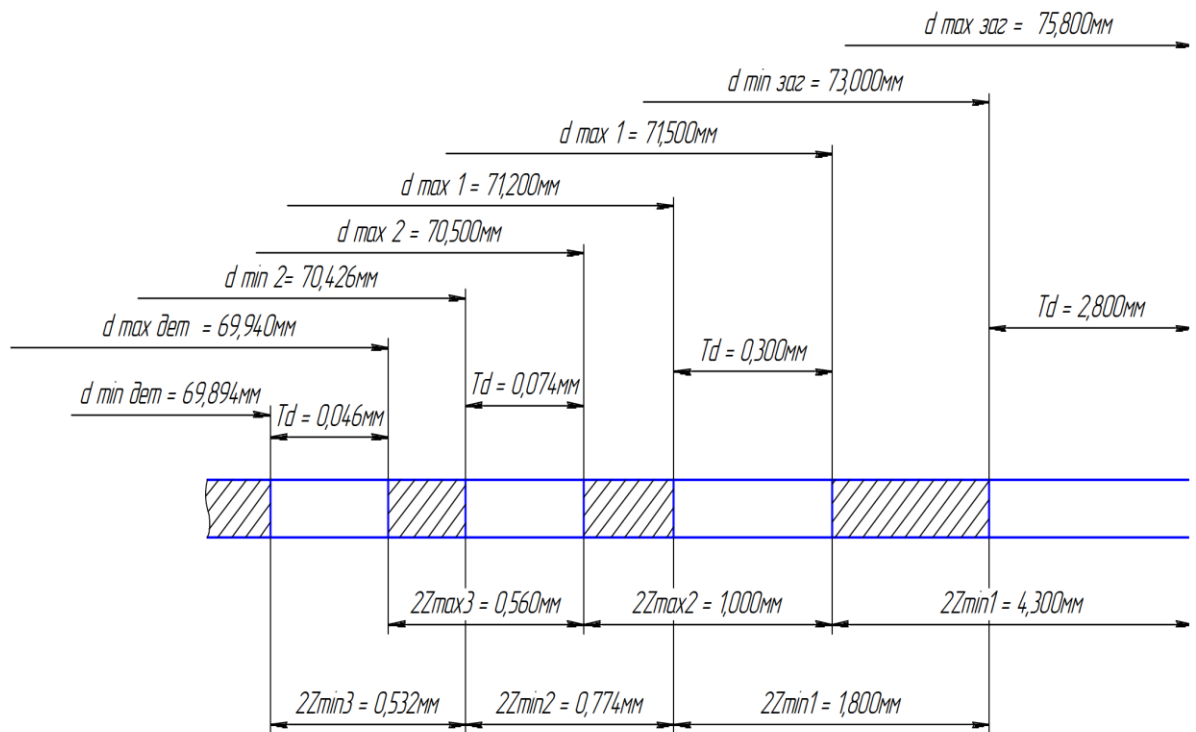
Схема граничного розташування припусків і допусків на обробку вала $\varnothing 70e8$
